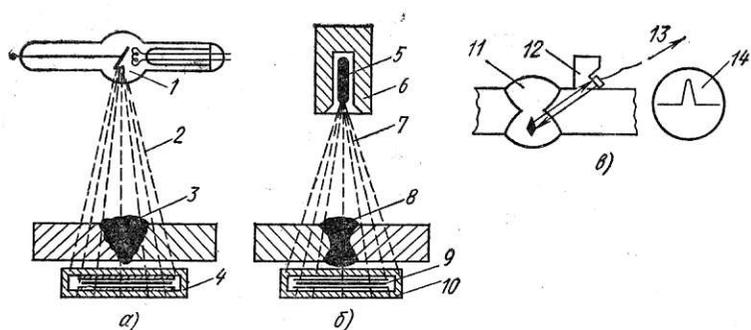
Методы контроля сварных соединений:
